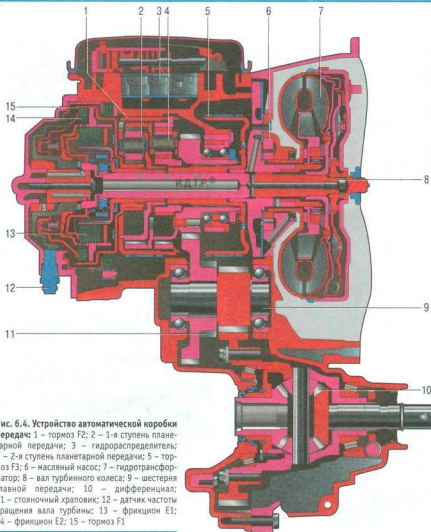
Устройство автоматической коробки передач: 1 – тормоз F2; 2 – 1-я ступень планетарной передачи; 3 – гидрораспределитель; 4 – 2-я ступень планетарной передачи; 5 – тормоз F3; 6 – масляный насос; 7 – гидротрансформатор; 8 – вал турбинного колеса; 9 – шестерня главной передачи; 10 – дифференциал; 11 – стояночный храповик; 12 – датчик частоты вращения вала турбины; 13 – фрикцион E1; 14 – фрикцион E2; 15 – тормоз F1
